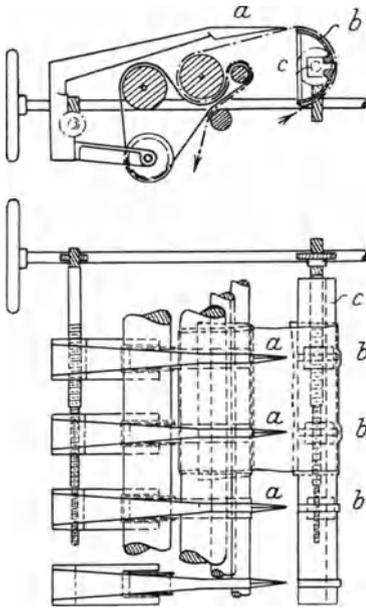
Vorrichtung zum Spannen des Gewebes an den Schneidstellen einer Viermessermaschine.
